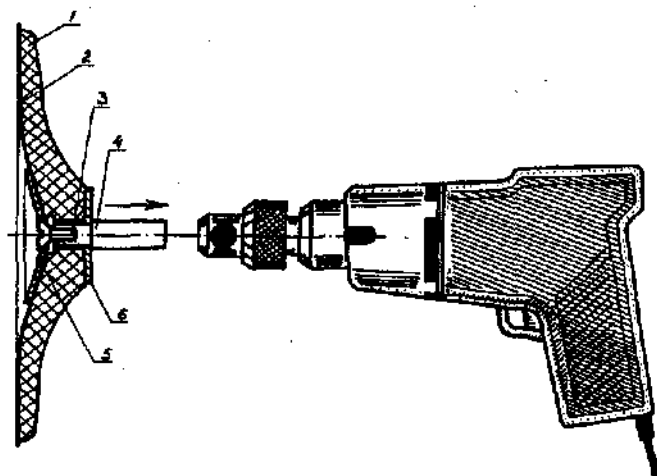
Конструкция круга для шлифовки плоскостей: 1 — лепесток резиновый; 2 — шлифовальная шкурка; 3 — винт; 4 — валик; 5 — шайба вогнутая; 6 — шайба плоская
